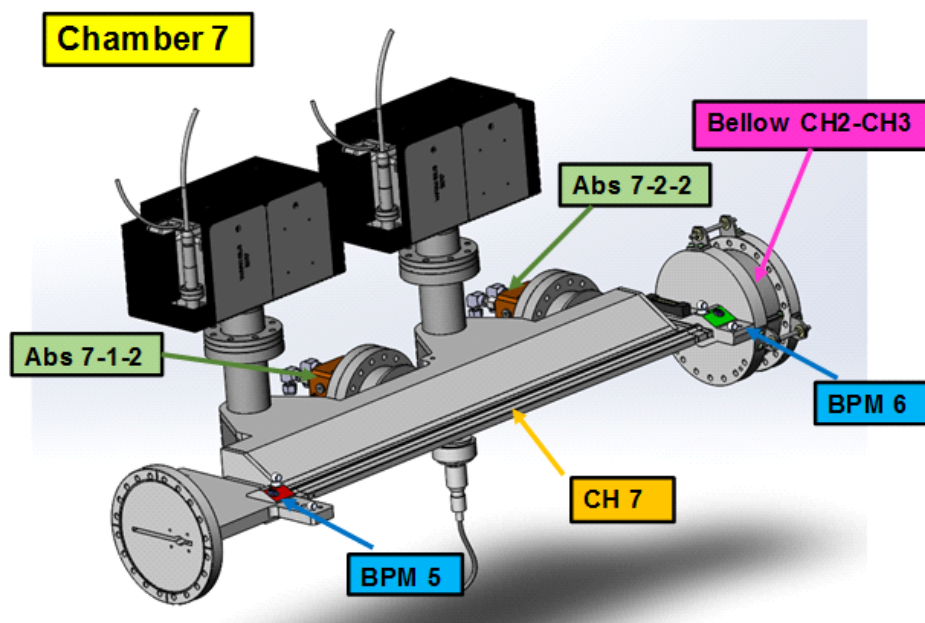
Вакуумная камера 7 – эскизный вид.
